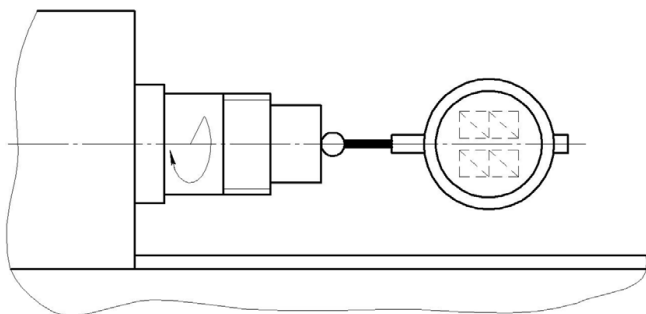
Схема установки индикатора для проверки осевого биения шпинделя
